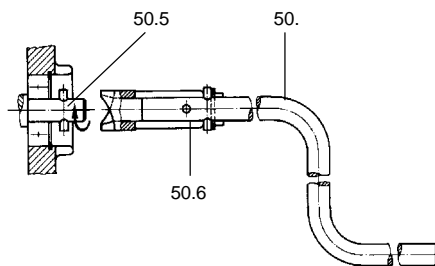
/1 Spannen der Einschaltfeder mittels Handkurbel
